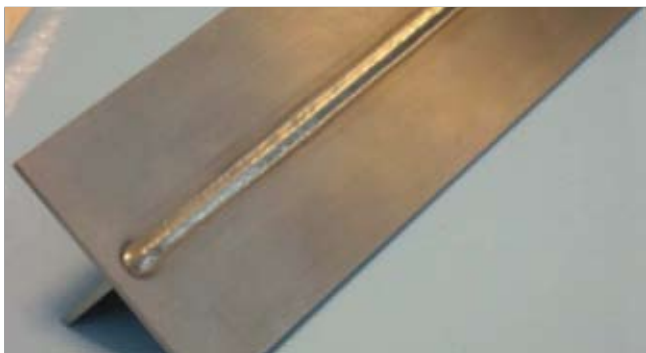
Цвет сварного шва ярко-серебряный. Данный цвет указывает на небольшое количество окисления (<20 частиц на миллион), говорящего о прочности конструкции
